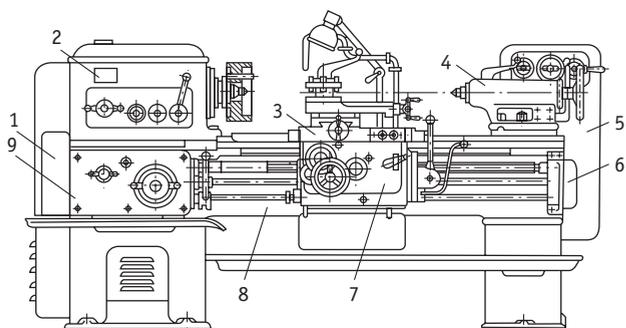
Универсальный токарно-винторезный станок 1К625: 1 – гитара сменных колес; 2 – передняя бабка; 3 – суппорт; 4 – задняя бабка; 5 – шкаф с электрооборудованием; 6 – электродвигатель быстрых перемещений суппорта; 7 – фартук; 8 – станина; 9 – коробка подач
